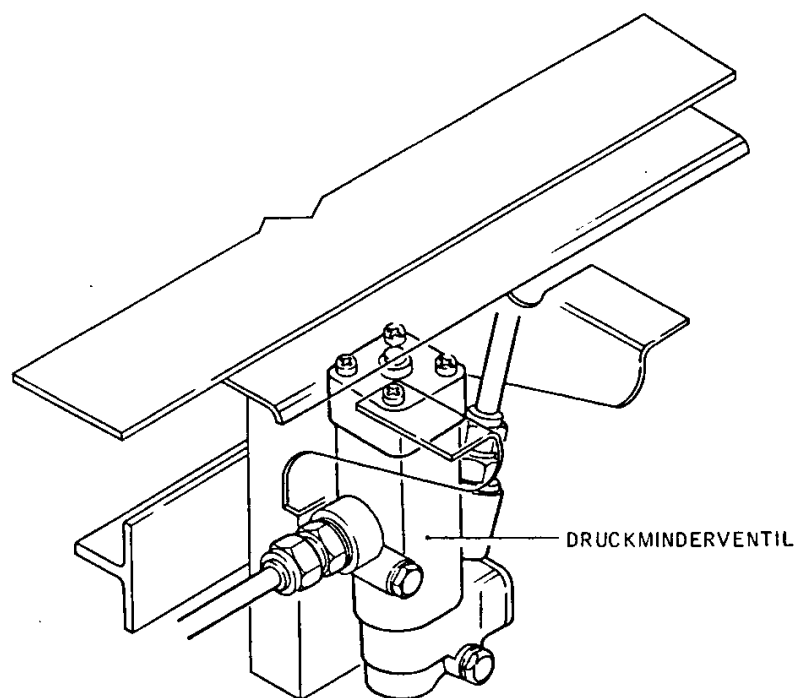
Ventil-Einbau im Fahrwerksschacht
